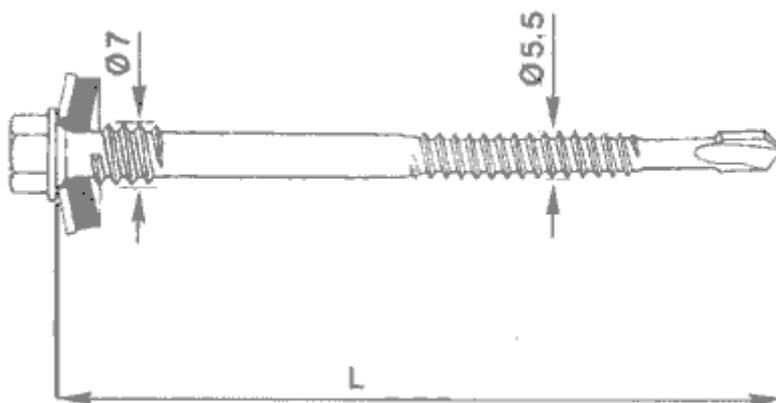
Конструкция винта для крепления "сэндвич"-панелей к металлической основе
